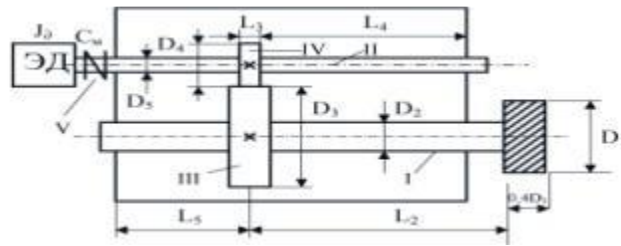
Чертеж одноступенчатого редуктора шпиндельного узла
